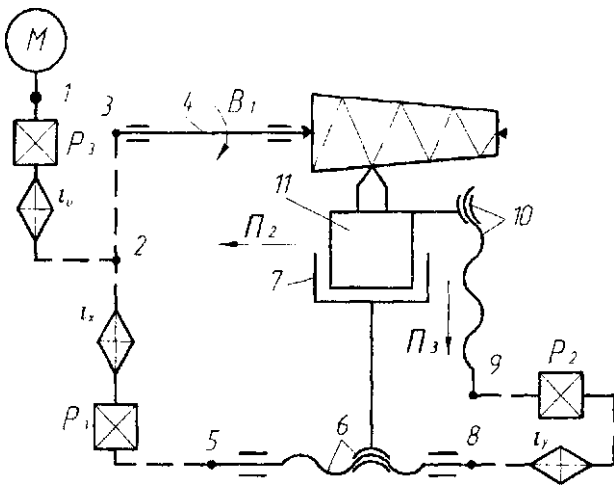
Структурная схема станка для нарезания резцом конической резьбы
